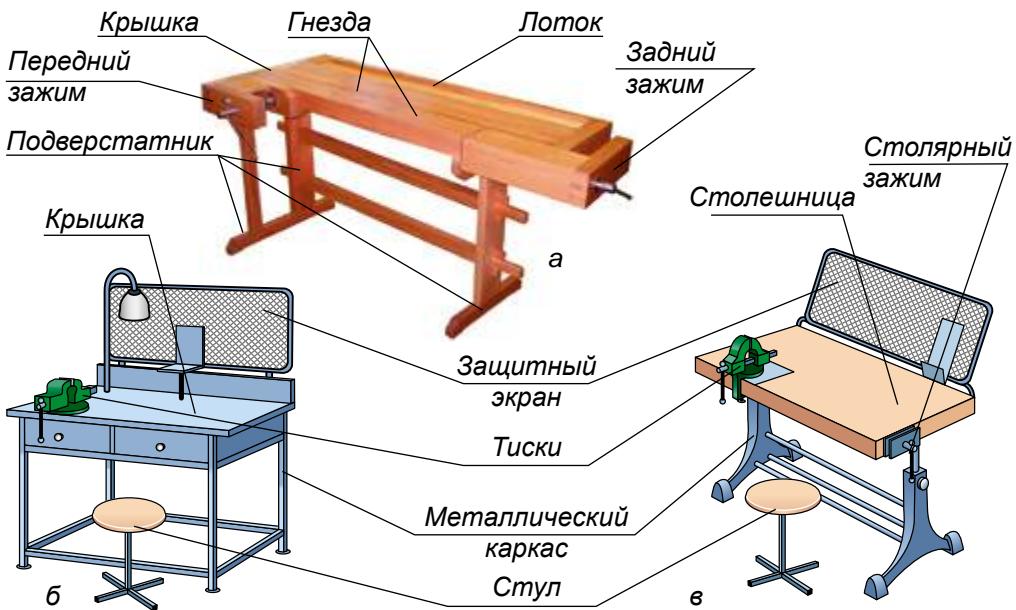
Верстаки: а – столярный; б – слесарный; в – комбинированный
